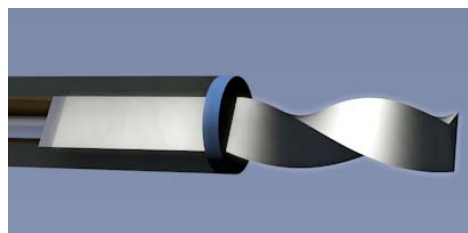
Выпрессовка заготовки с повторным скручиванием
